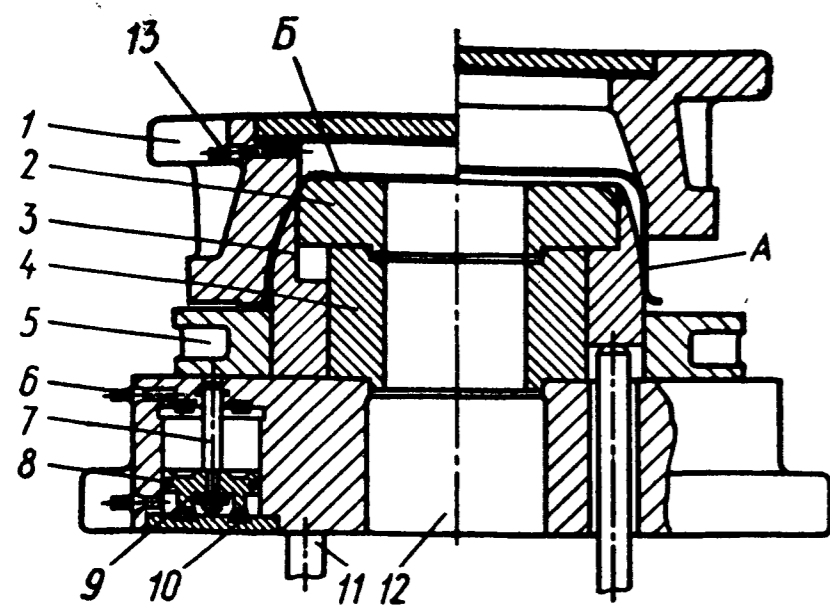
Штамп для вытяжки детали с криволинейной образующей
